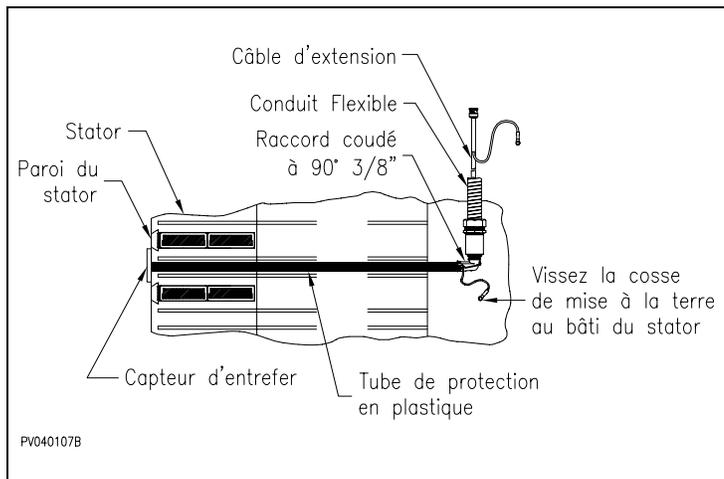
Vue d'ensemble du tube de protection, raccord coudé et conduit flexible
